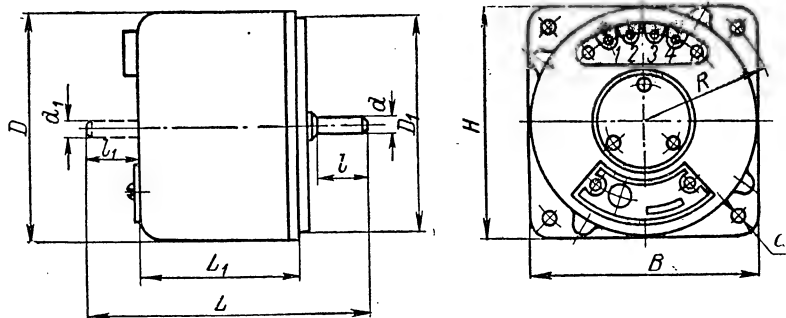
Электродвигатели в закрытом исполнении типов РСД-413-2 и РСД-421-2 с одним выступающим концом вала и РСД-412-2 и РСД-422-2 с двумя выступающими концами вала (второй конец вала показан пунктиром)
